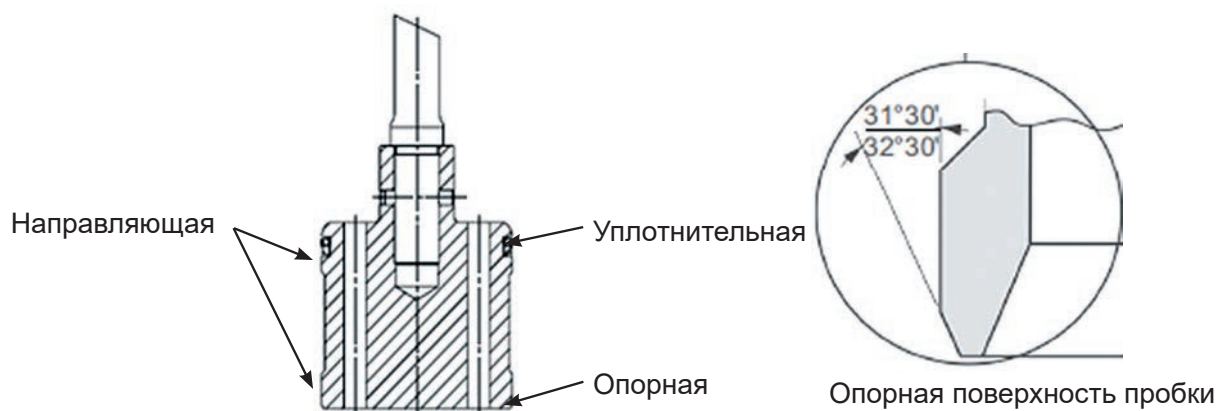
Направляющая, уплотнительная и опорная поверхности пробки
